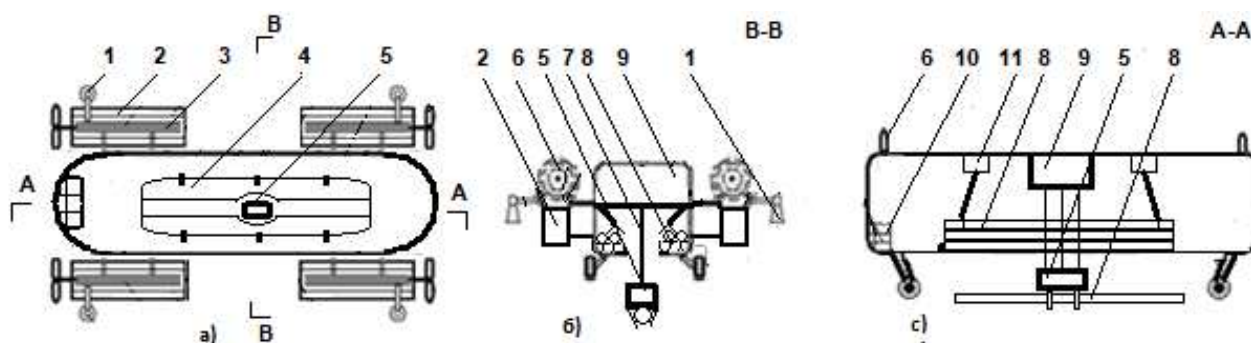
Схема авиационной платформы для трелёвки [13]: 1 — сопла точного позиционирования; 2 — эжекторный усилитель тяги; 3 — ПудД; 4 — створки люка загрузки; 5 — подвес подъёмника; 6 — винт изменяемого шага самолётного типа; 7 — захваты для груза; 8 — заготовленная древесина; 9 — грузовая лебёдка; 10 — кабина управления; 11 — манипулятор
